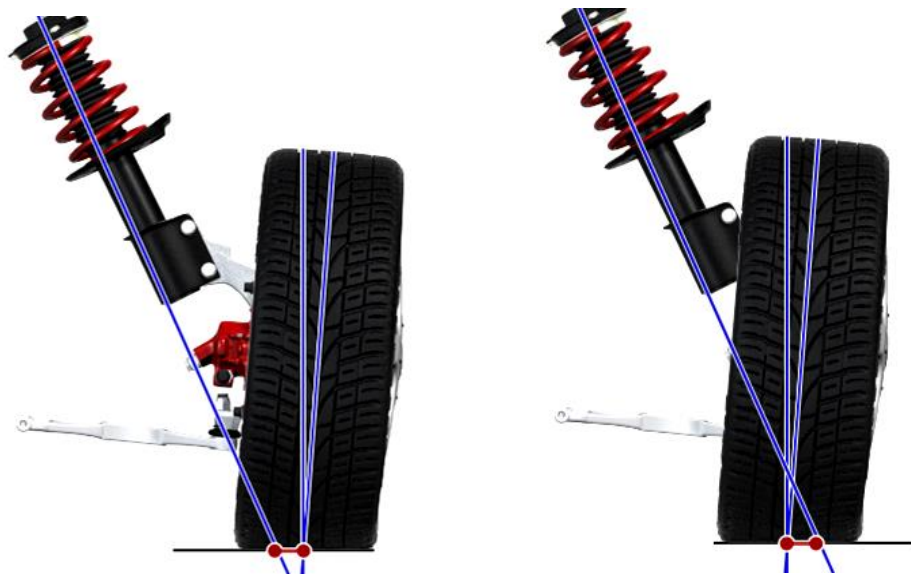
Радіус плеча обкатки: позитивний і негативний.
